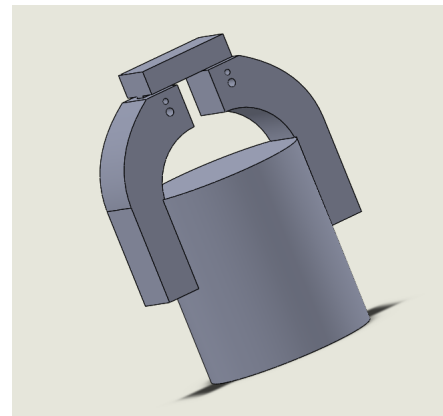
Desenho do conjunto: garra, extensão e objeto, dimensionada em SolidWorks
